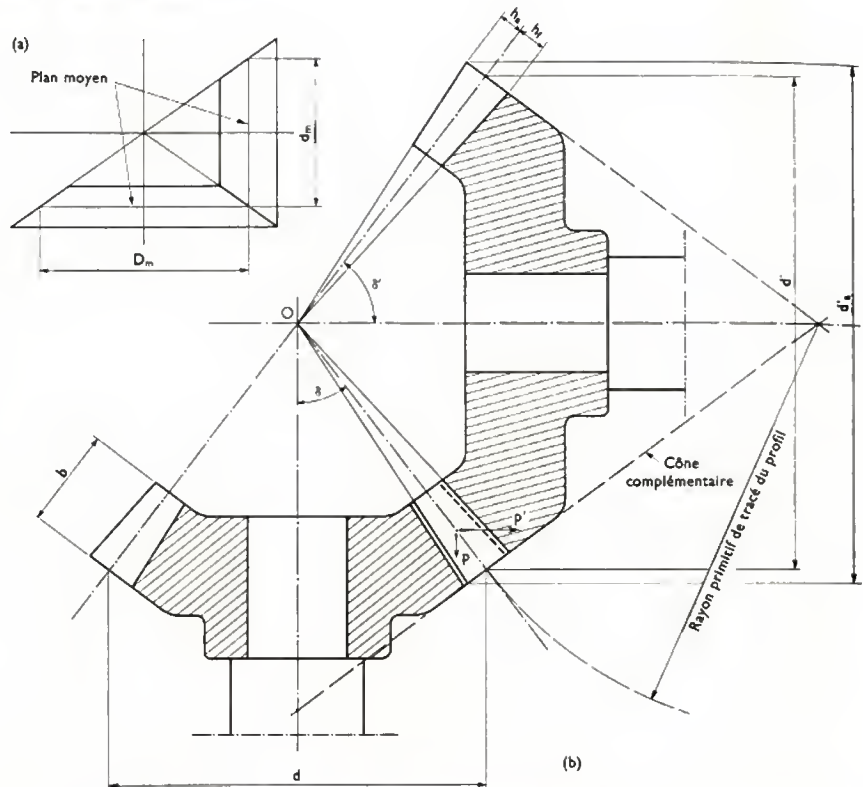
Engrenage conique à denture droite (Mobil Oil)
